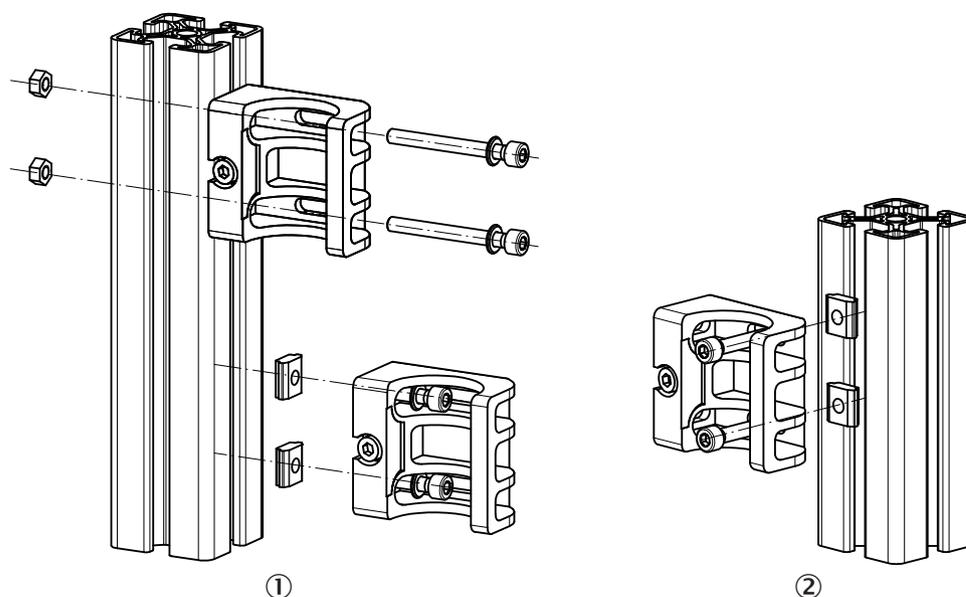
Монтаж креплений FlexFix на раме профиля
